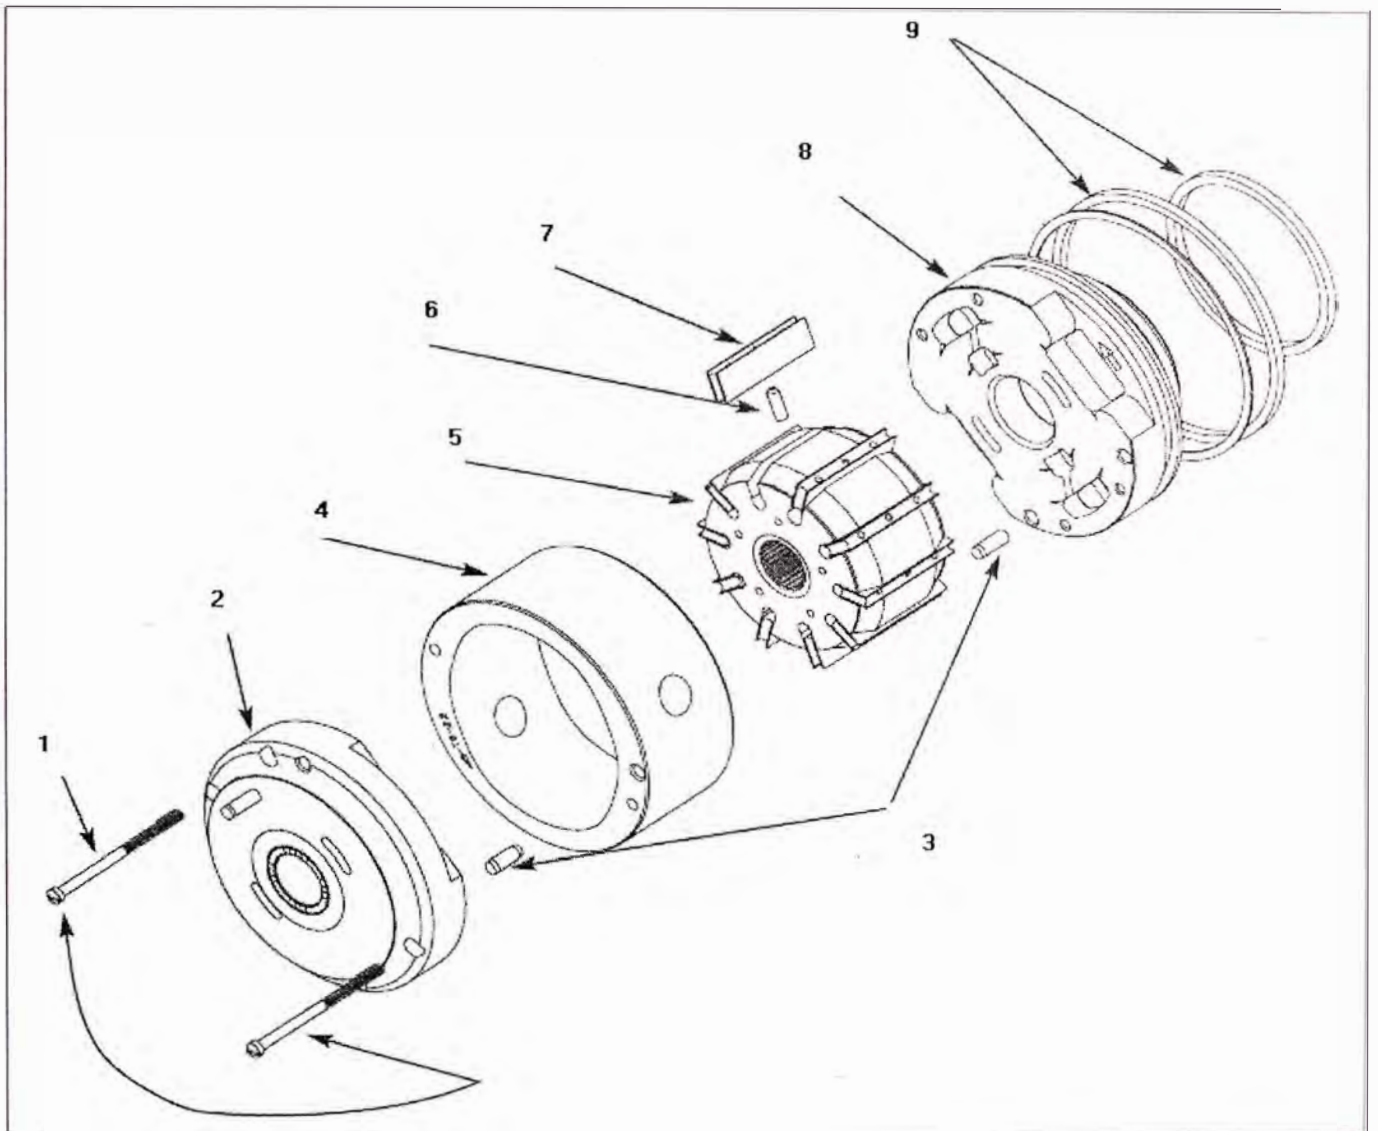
Despiece de Cartucho: (1) Tornillos,(2) Plato Posterior, (3) Pin, (4) Anillo, (5) Rotor, (6) pin, (7) Vane, (8) Plato de presión, (9) Sellos.
